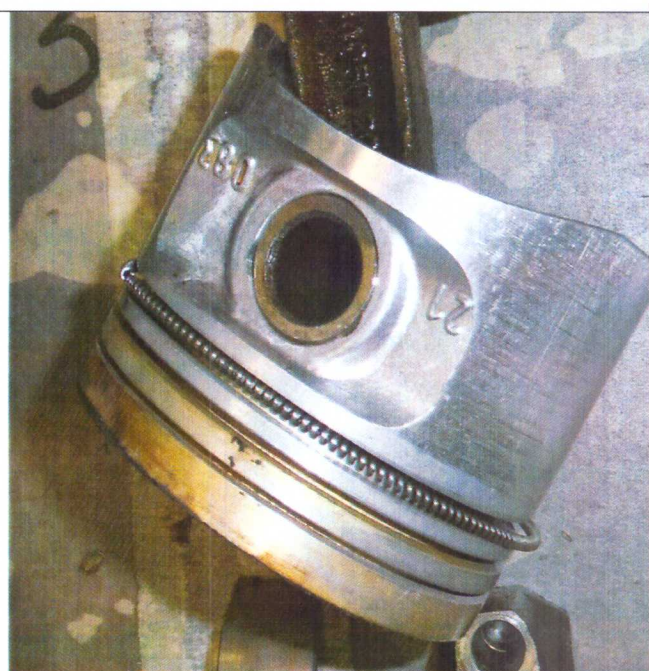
Внешний вид боковой поверхности поршня второго цилиндра по окончании длительных испытаний двигателя при работе на базовом масле Castrol EDGE
